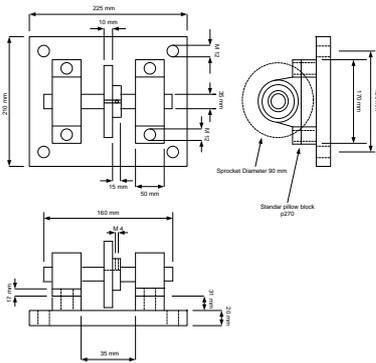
Desain Support Unit Motor Induksi 3 Fasa
